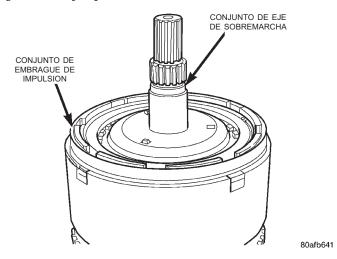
Conjunto de embrague de impulsión TRANSEJE— ENSAMBLAJE
